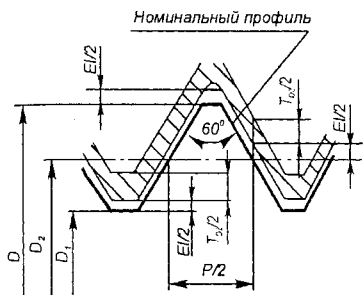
Расположение полей допусков резьбовой посадки с зазором
